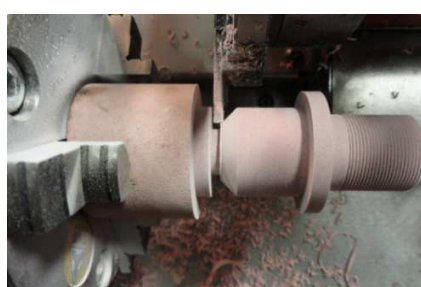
Hrubování Ø 24 při realné výrobě
